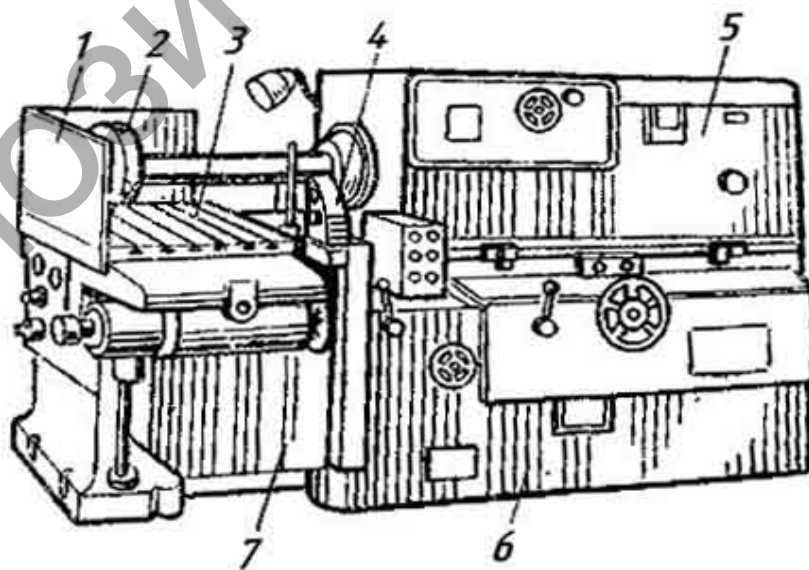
Общий вид планетарного внутришлифовального станка модели MB6020
